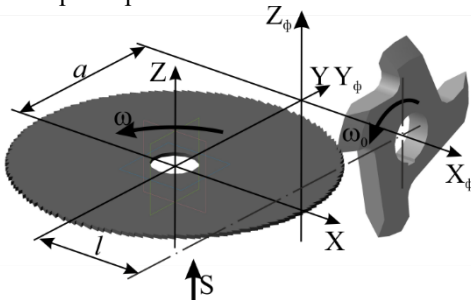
Схема обробки на зубофрезерному верстаті
